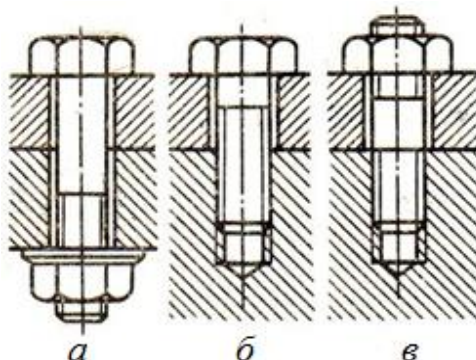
Виды резьбовых соединений: а – болтовое; б – винтовое; в – при помощи шпильки
